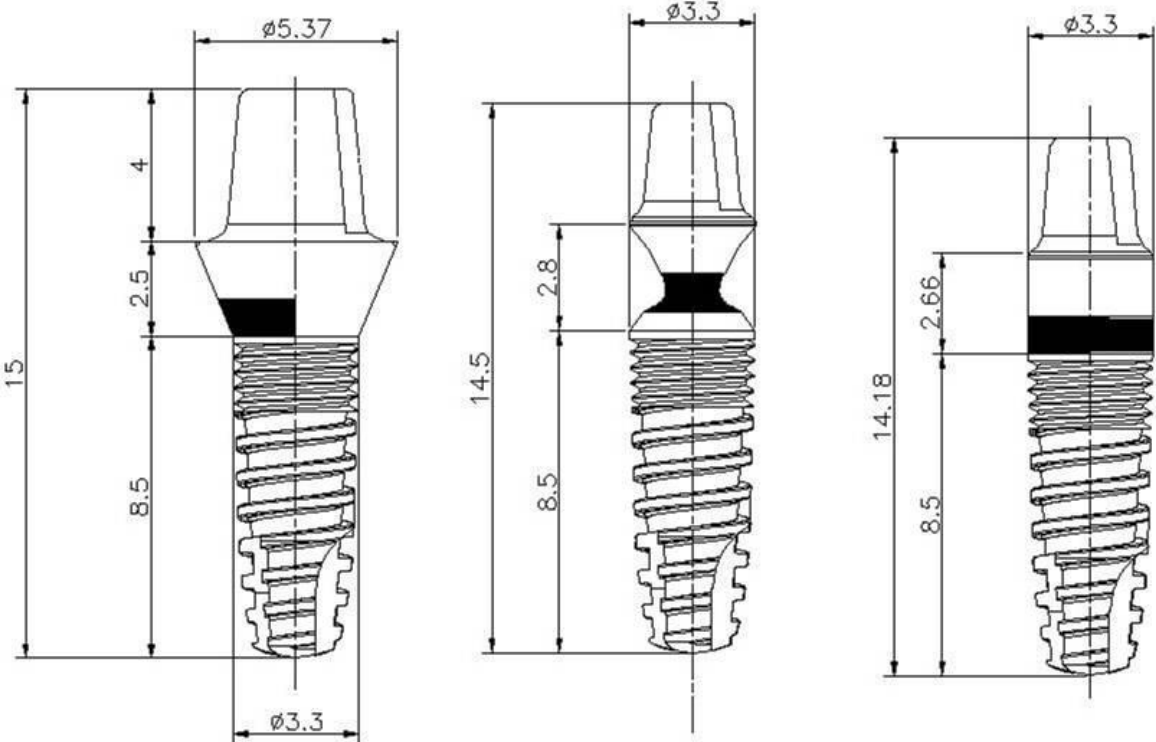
Piliers implantaires convexe, concave et droit (de gauche à droite).
